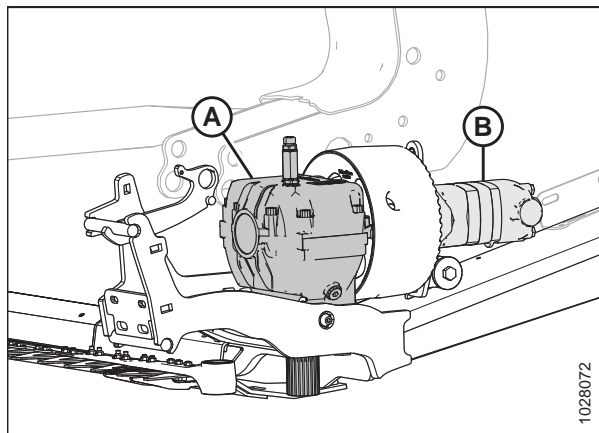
Показан левый редуктор привода ножа (правый аналогичен левому)
